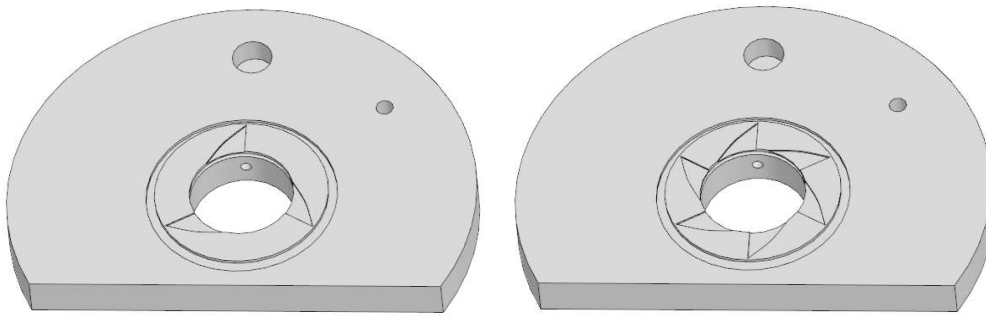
Конструкция упорных подшипников с тремя и шести сегментами
